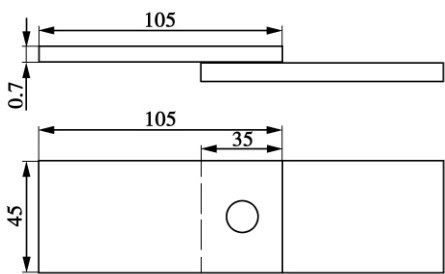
电阻点焊接头剪切试样 (mm)
